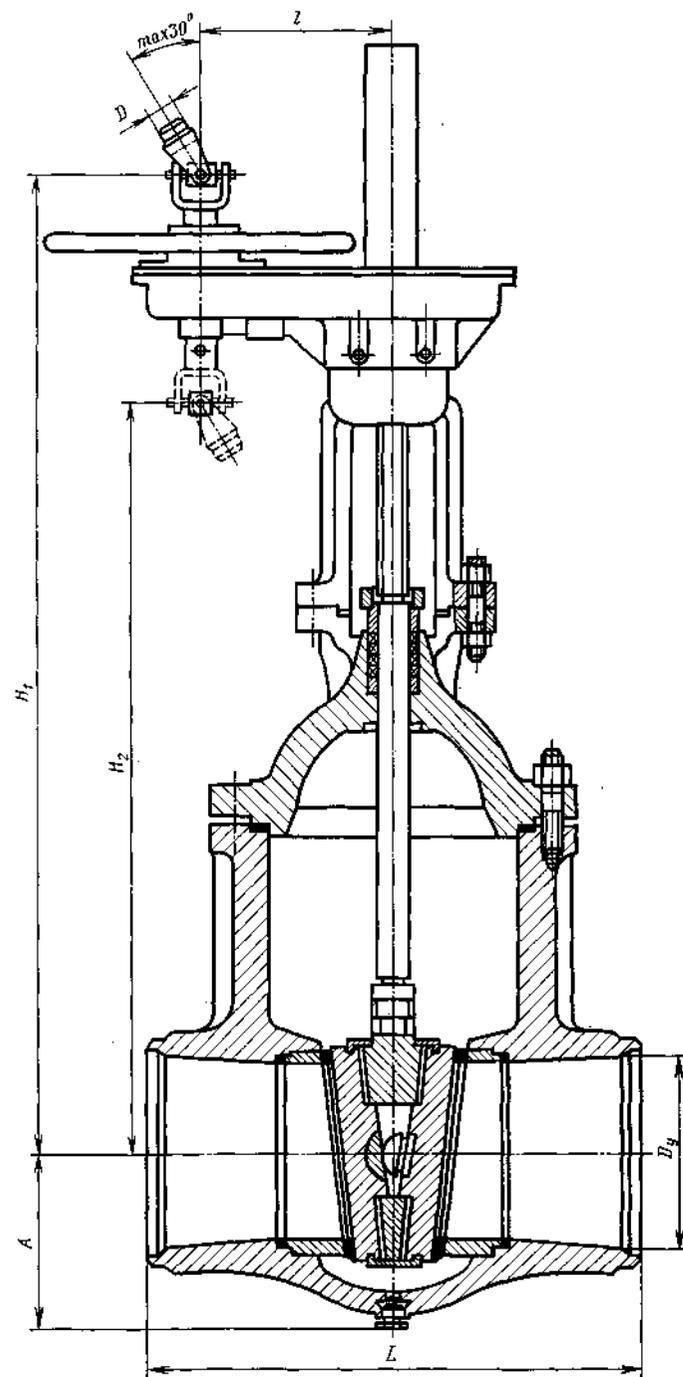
Задвижка с приводной головкой с цилиндрическим зубчатым редуктором Ду, 350, 400 и 450 серии 850
